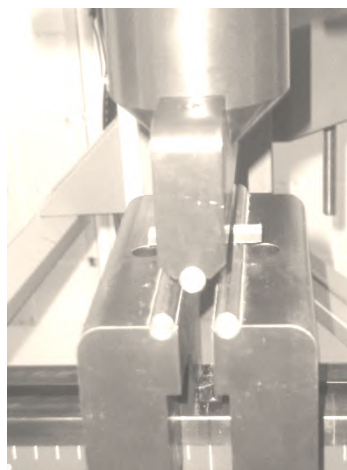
Испытываемый образец под плавно нарастающей нагрузкой
